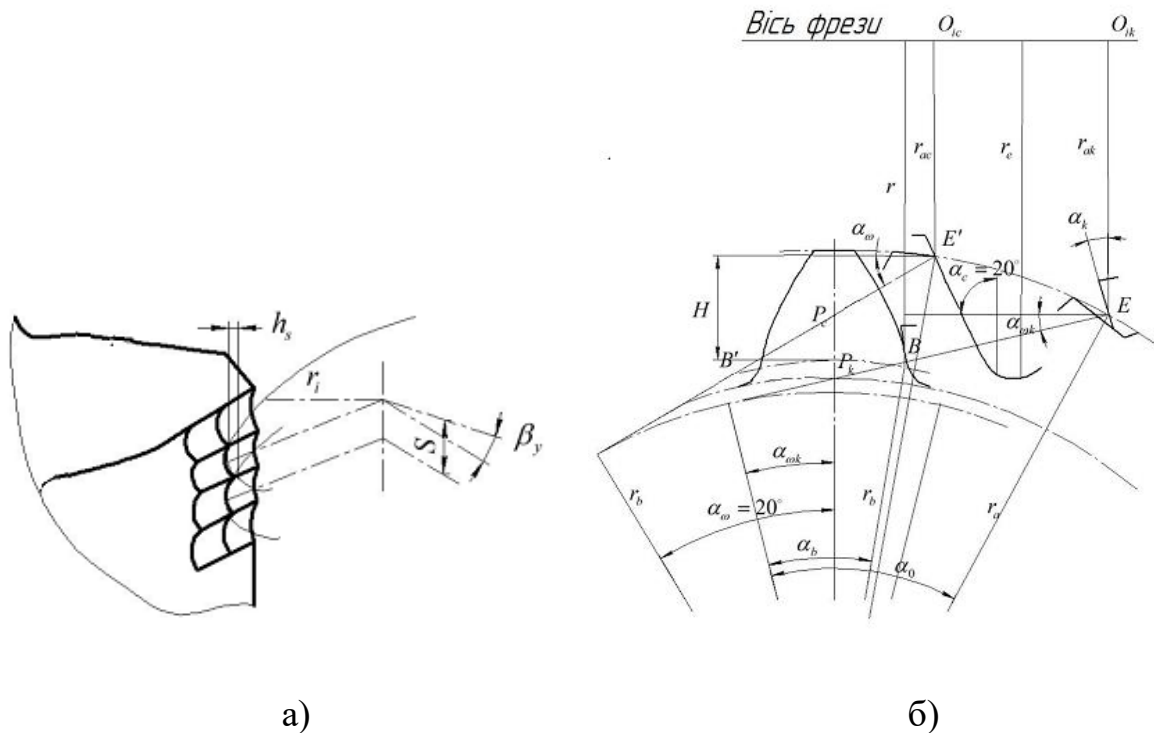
Визначення розрахункової (геометричної) величини хвилястості обробленої поверхні: а - схема утворення хвилі на бічній поверхні зуба колеса; б - визначення розміру радіусів обертання точок зубів фрези, що формують хвилю біля вершини зуба колеса
